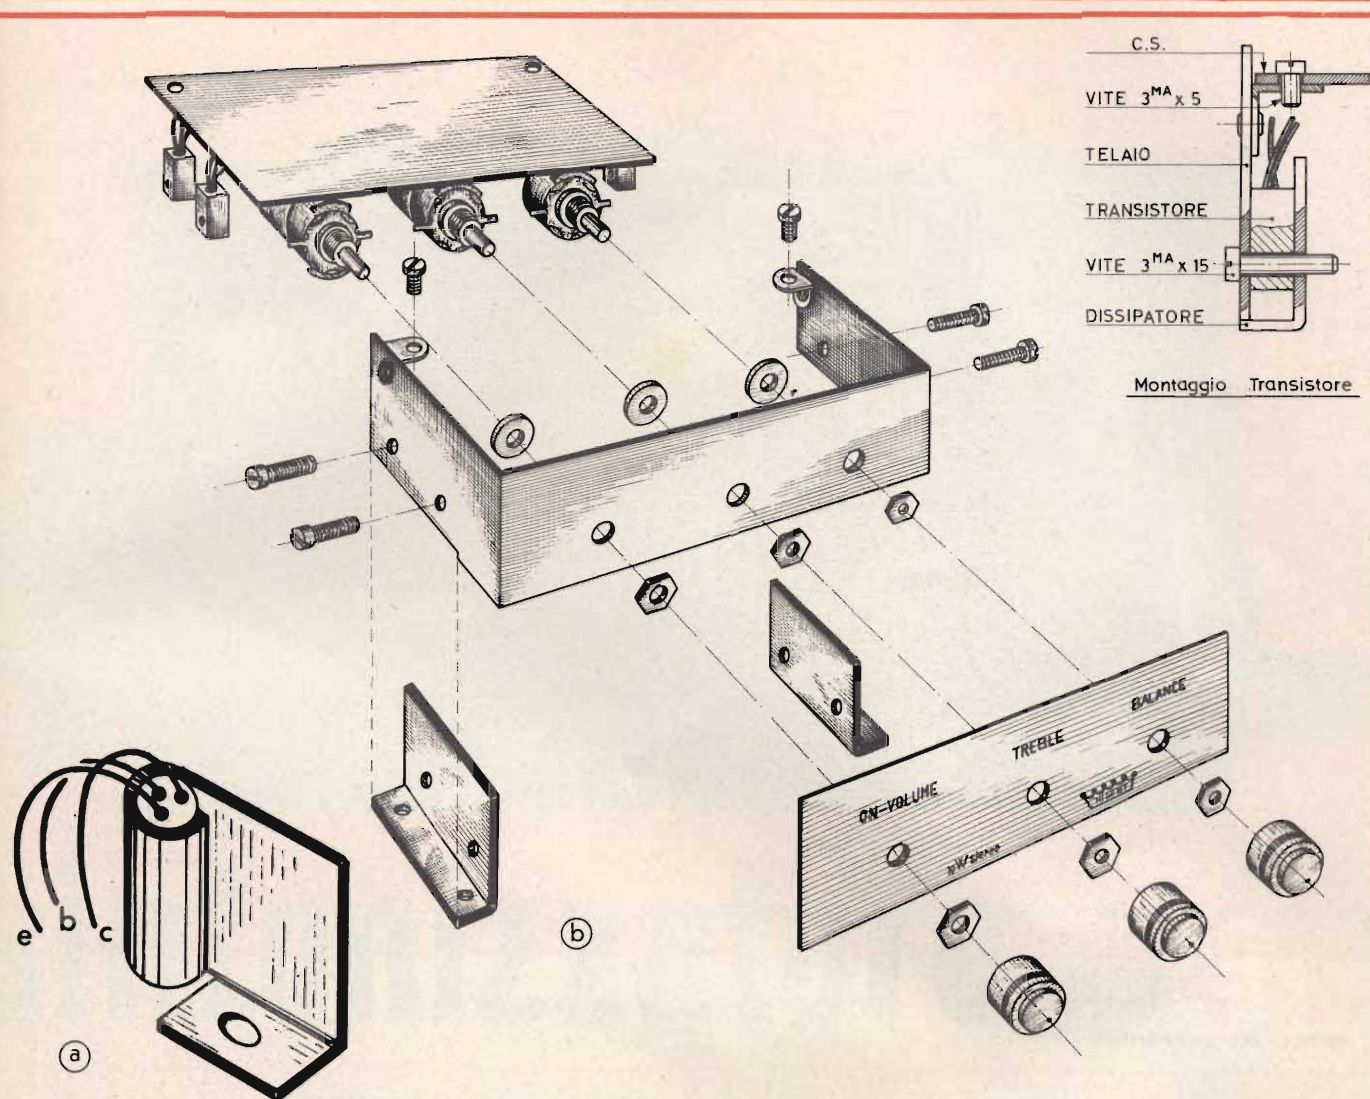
a - Disposizione del transistor TR3 nel dissipatore.
